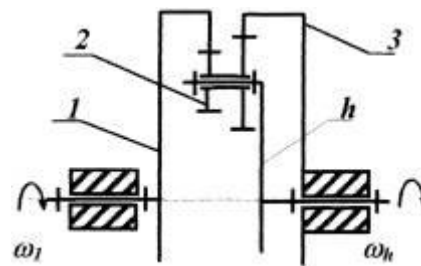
Двухрядный планетарный механизм с двумя внутренними зацеплениями
